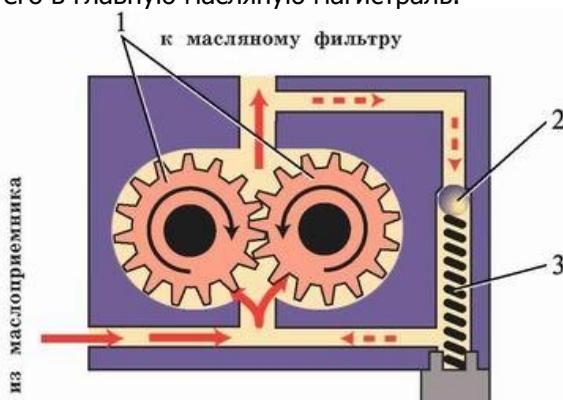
Схема работы масляного насоса: 1 – шестерни масляного насоса; 2 – редукционный клапан; 3 – пружина
